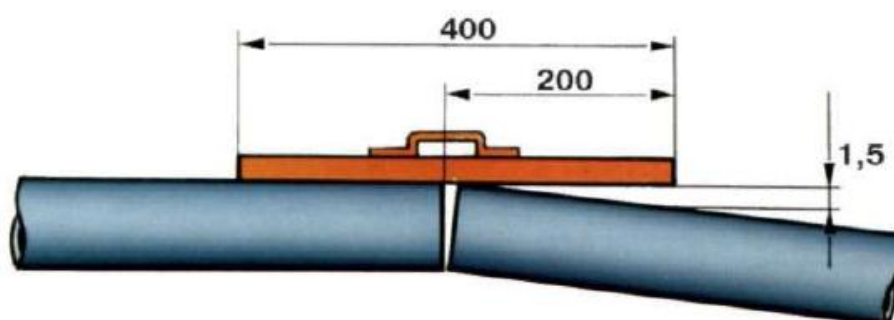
Проверка прямолинейности при сборке стыка труб
